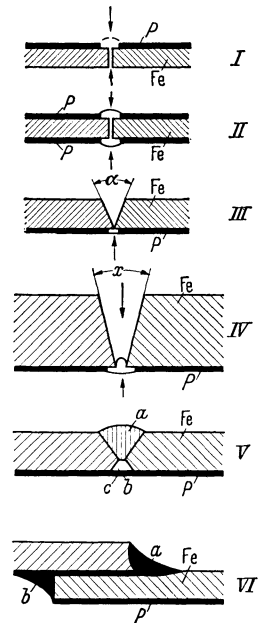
Vorbereitung plattierter Bleche zum Schweißen.
